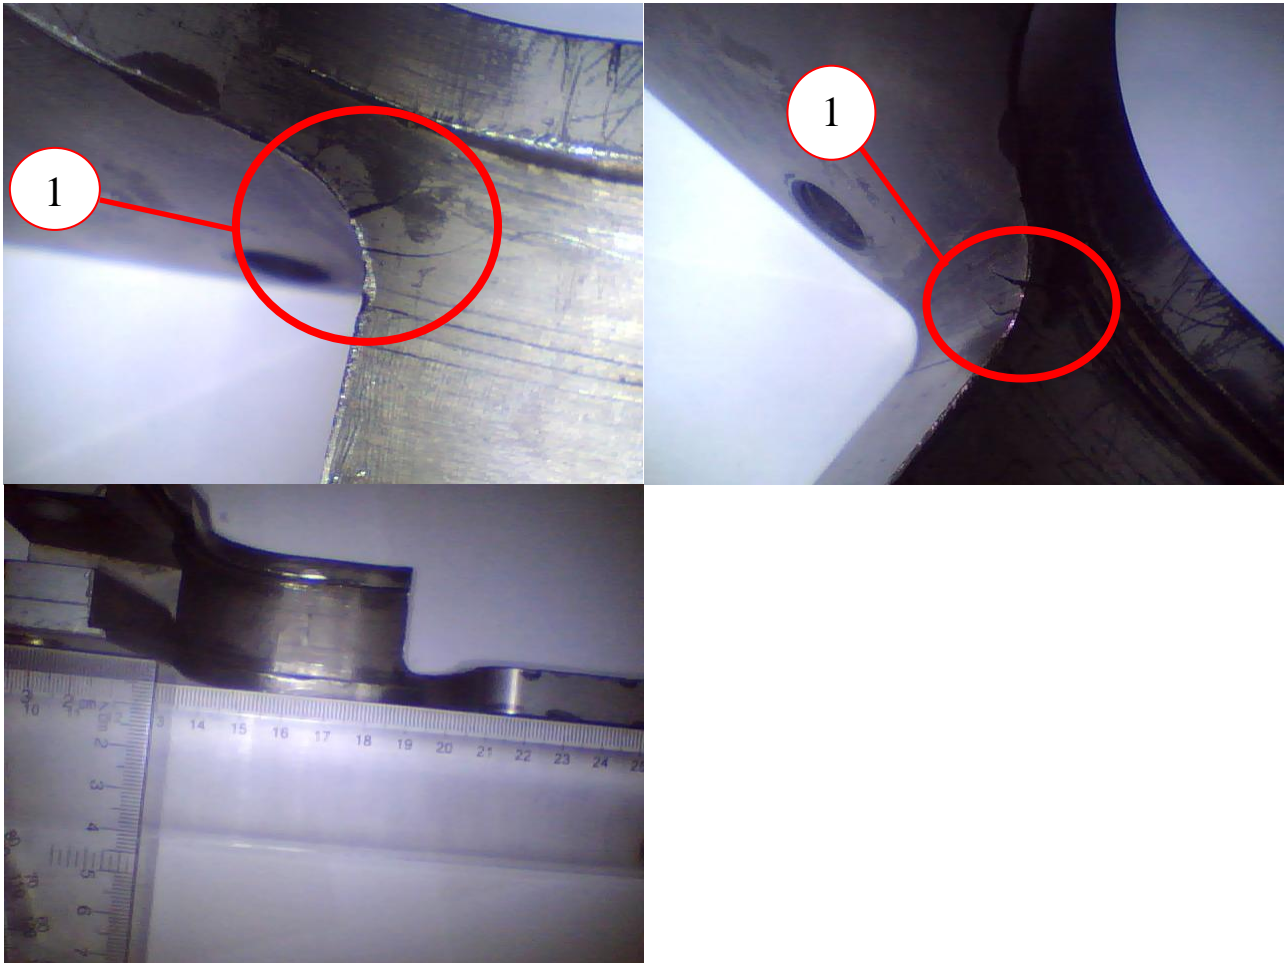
Fissuration et déformation du premier support porte arbre de bobinage
